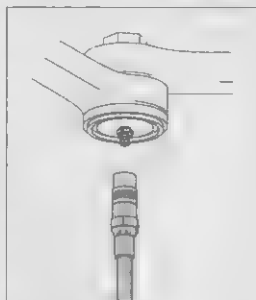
Смазочный шприц с переходником и пресс-масленка
